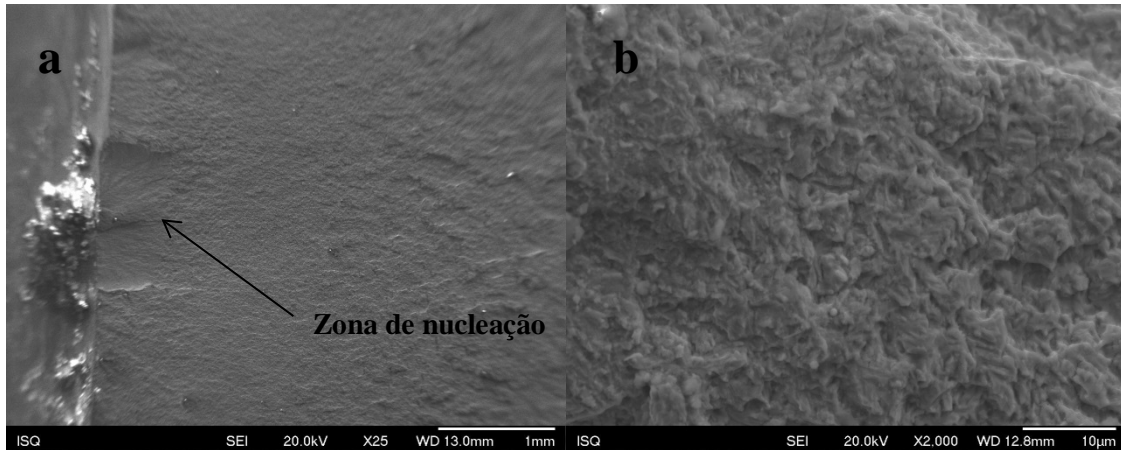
Ilustração sobre superfície de fratura do provete aço S460 M; a) Superfície do provete, b) Zona de iniciação de fadiga.
